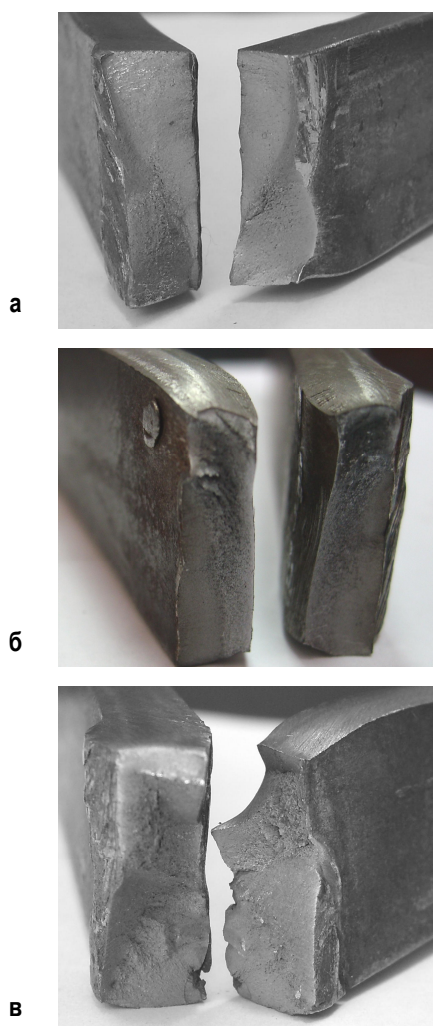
Излом сварного соединения после усталостных испытаний (а – образец серии №9; б – образец серии №12; в – образец серии №11)
